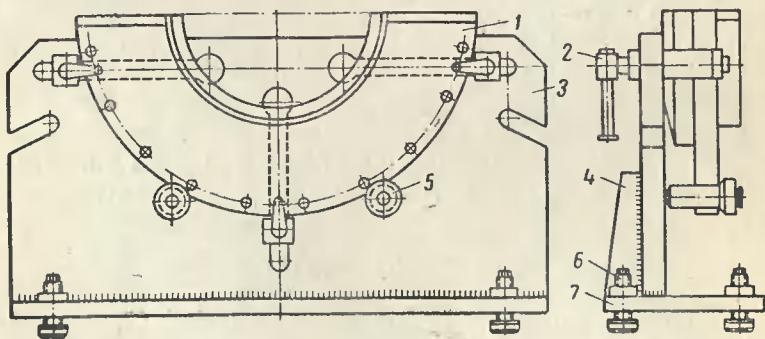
Станок для установки деталей уплотнения при слесарной обработке.
